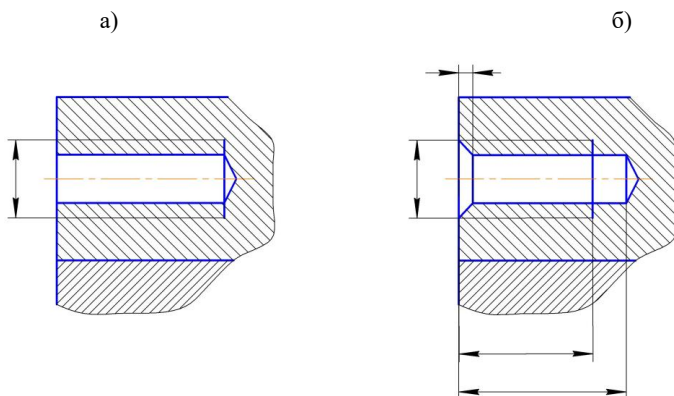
Изображение глухого отверстия на чертеже общего вида и чертеже детали
